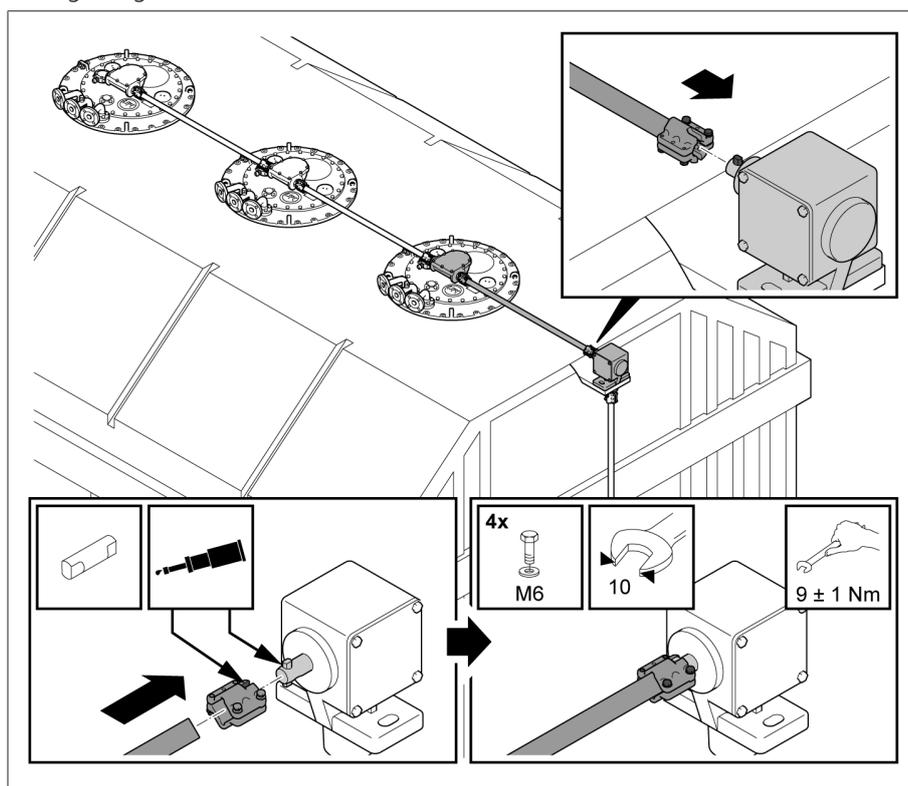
Eixo de transmissão entre a caixa de reenvio e a caixa de engrenagem
